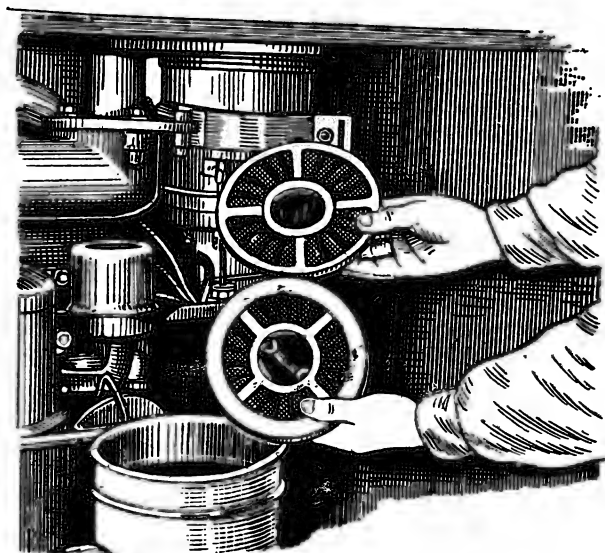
Установка сетчатых элементов в корпусе воздухоочистителя
